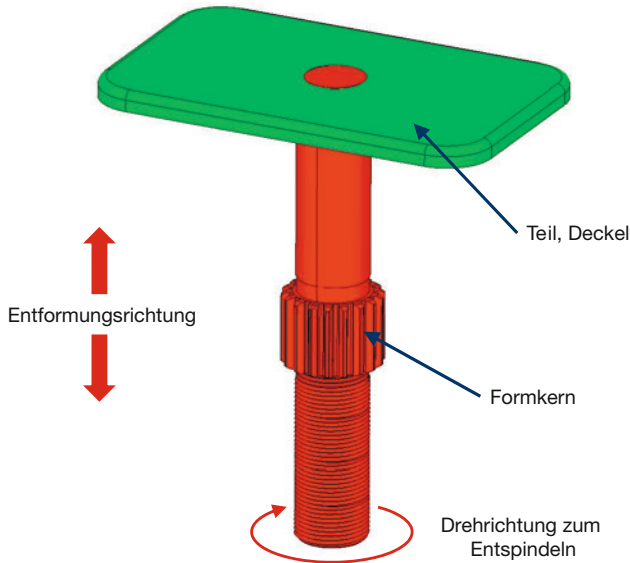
Werkzeug für Deckel mit Außengewinde
